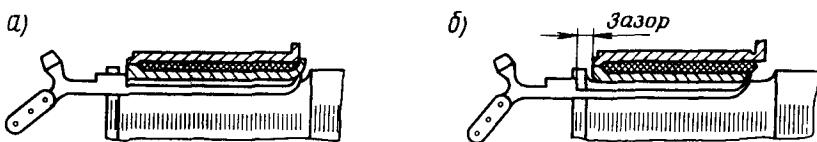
Положение выступа универсального крючка-шаблона относительно торца подшипника:
